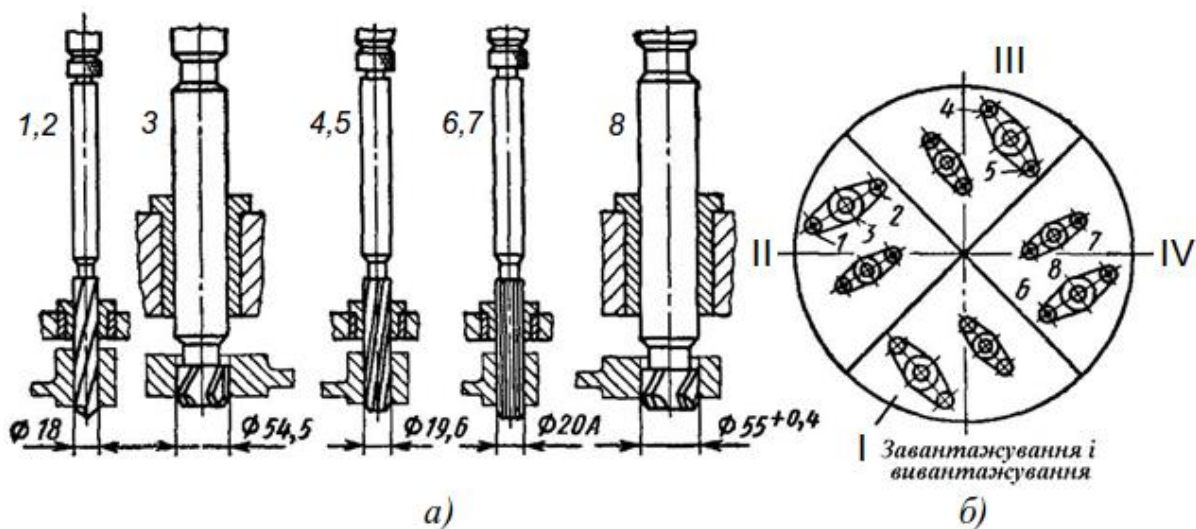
Схема обробки отворів у здвоєній заготовці плоских вилок на агрегатному верстаті:
